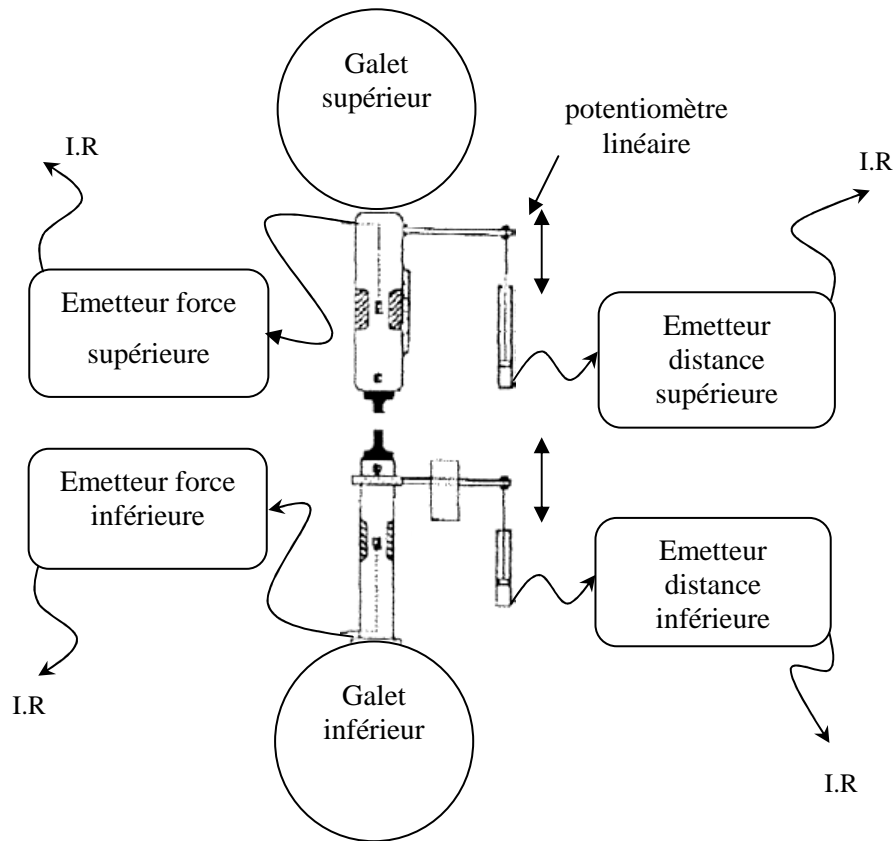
Vue de l'implantation des équipements sur la partie mobile de la machine rotative
